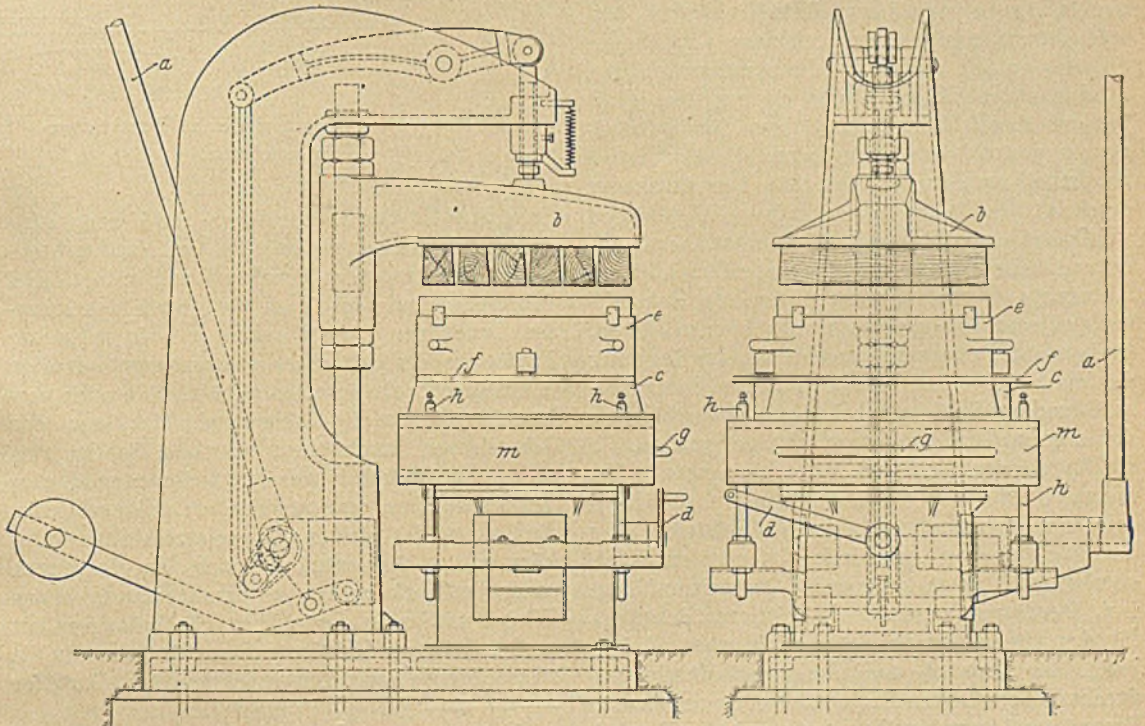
Hand-Preßformmaschine für Bremsklötze.
